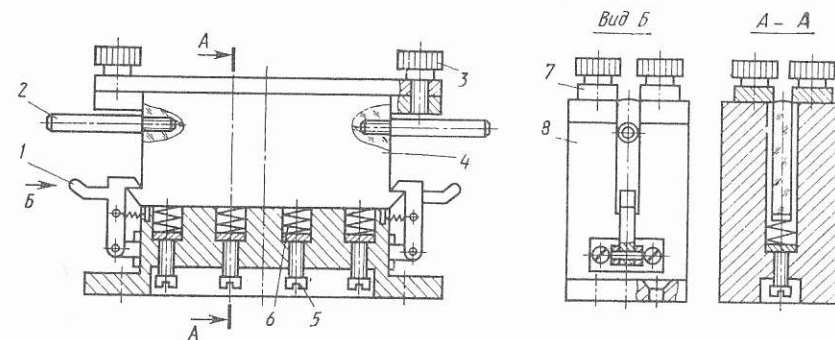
Приспособление для лазерной сварки узких ленточных проводников
